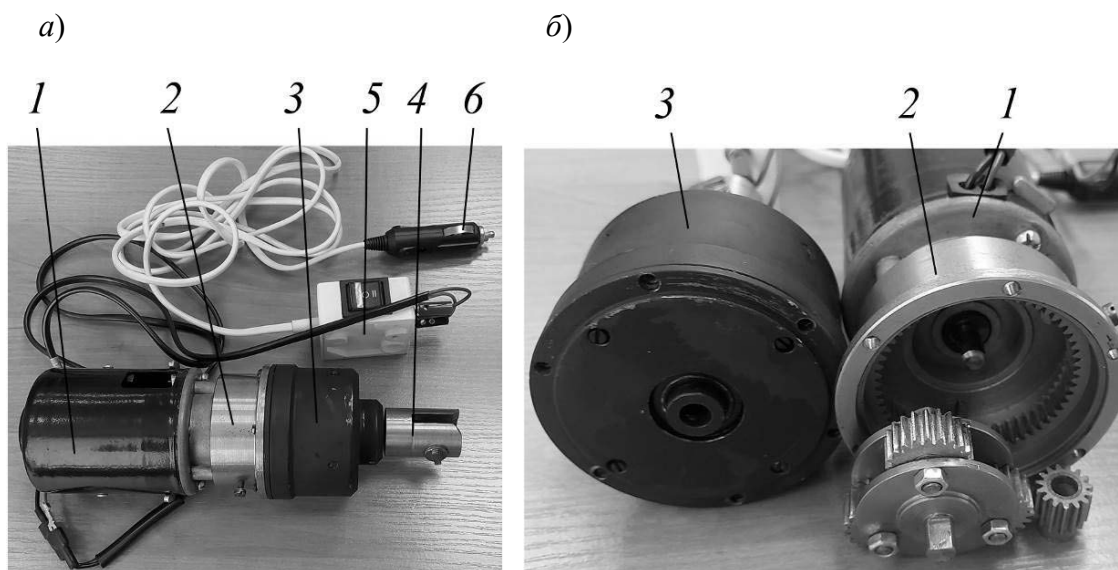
Электромеханический привод с питанием от электросистемы автомобиля: а – общий вид; б – редукторные узлы; 1 – двигатель постоянного тока; 2 – редукторный модуль с планетарной передачей; 3 – редукторный модуль с СРП; 4 – рабочий орган на приводном валу; 5 – выключатель, в т. ч. для обеспечения реверса вращения; 6 – штекер для автомобильного «прикуривателя»
